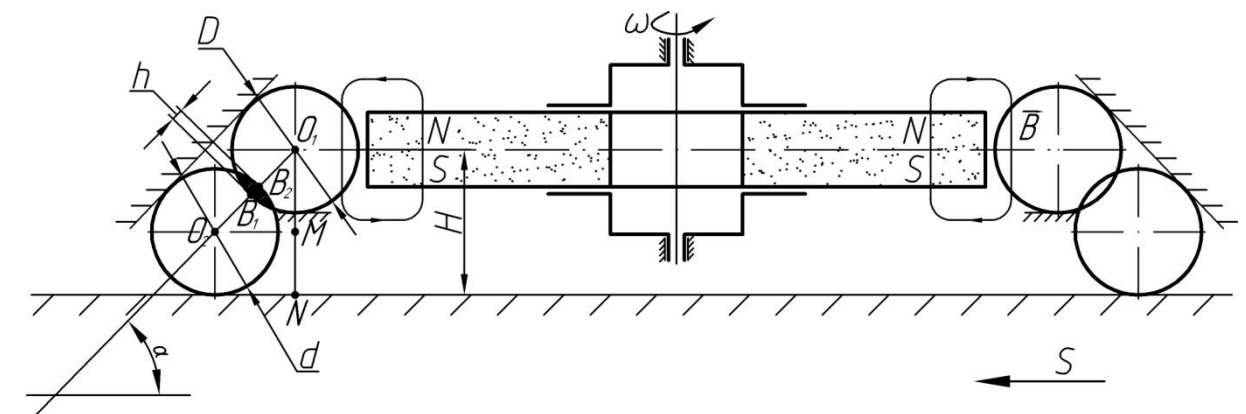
Схема магнитно-динамического накатывания плоских поверхностей деталей машин
